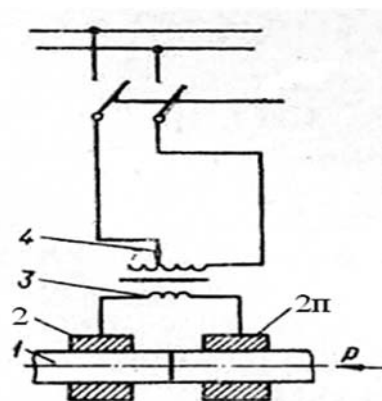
Схема стыковой сварки давлением
